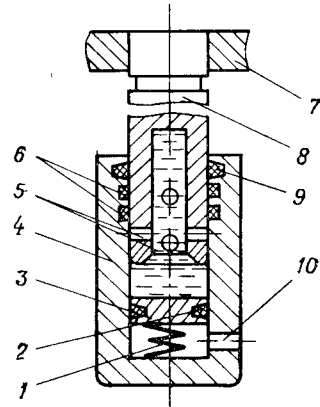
Схема направляющей пары штампа с принудительной подачей смазки
